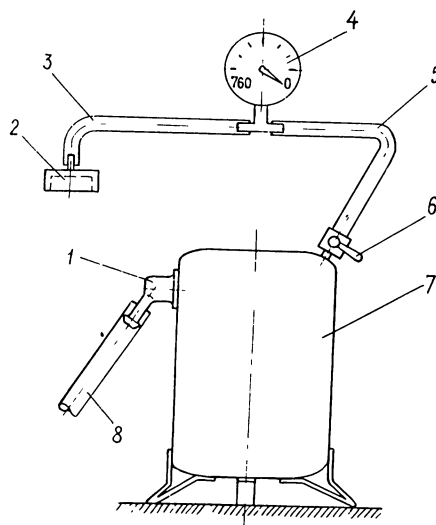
Приспособление для контроля герметичности первичной манжеты первичного поршня главного тормозного цилиндра: 1–обратный клапан; 2–крышка бачка; 3,5,8–шланги; 4–вакуумметр; 6–запорный кран; 7–ресивер
